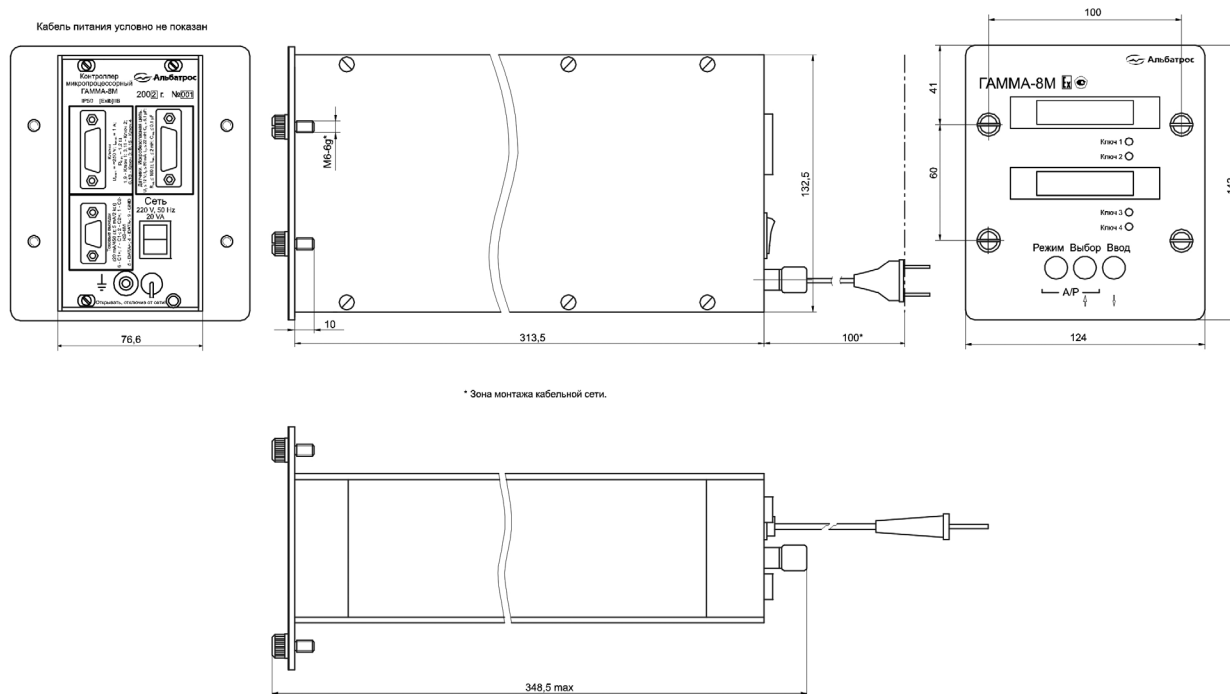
Внешний вид и габаритные размеры прибора
